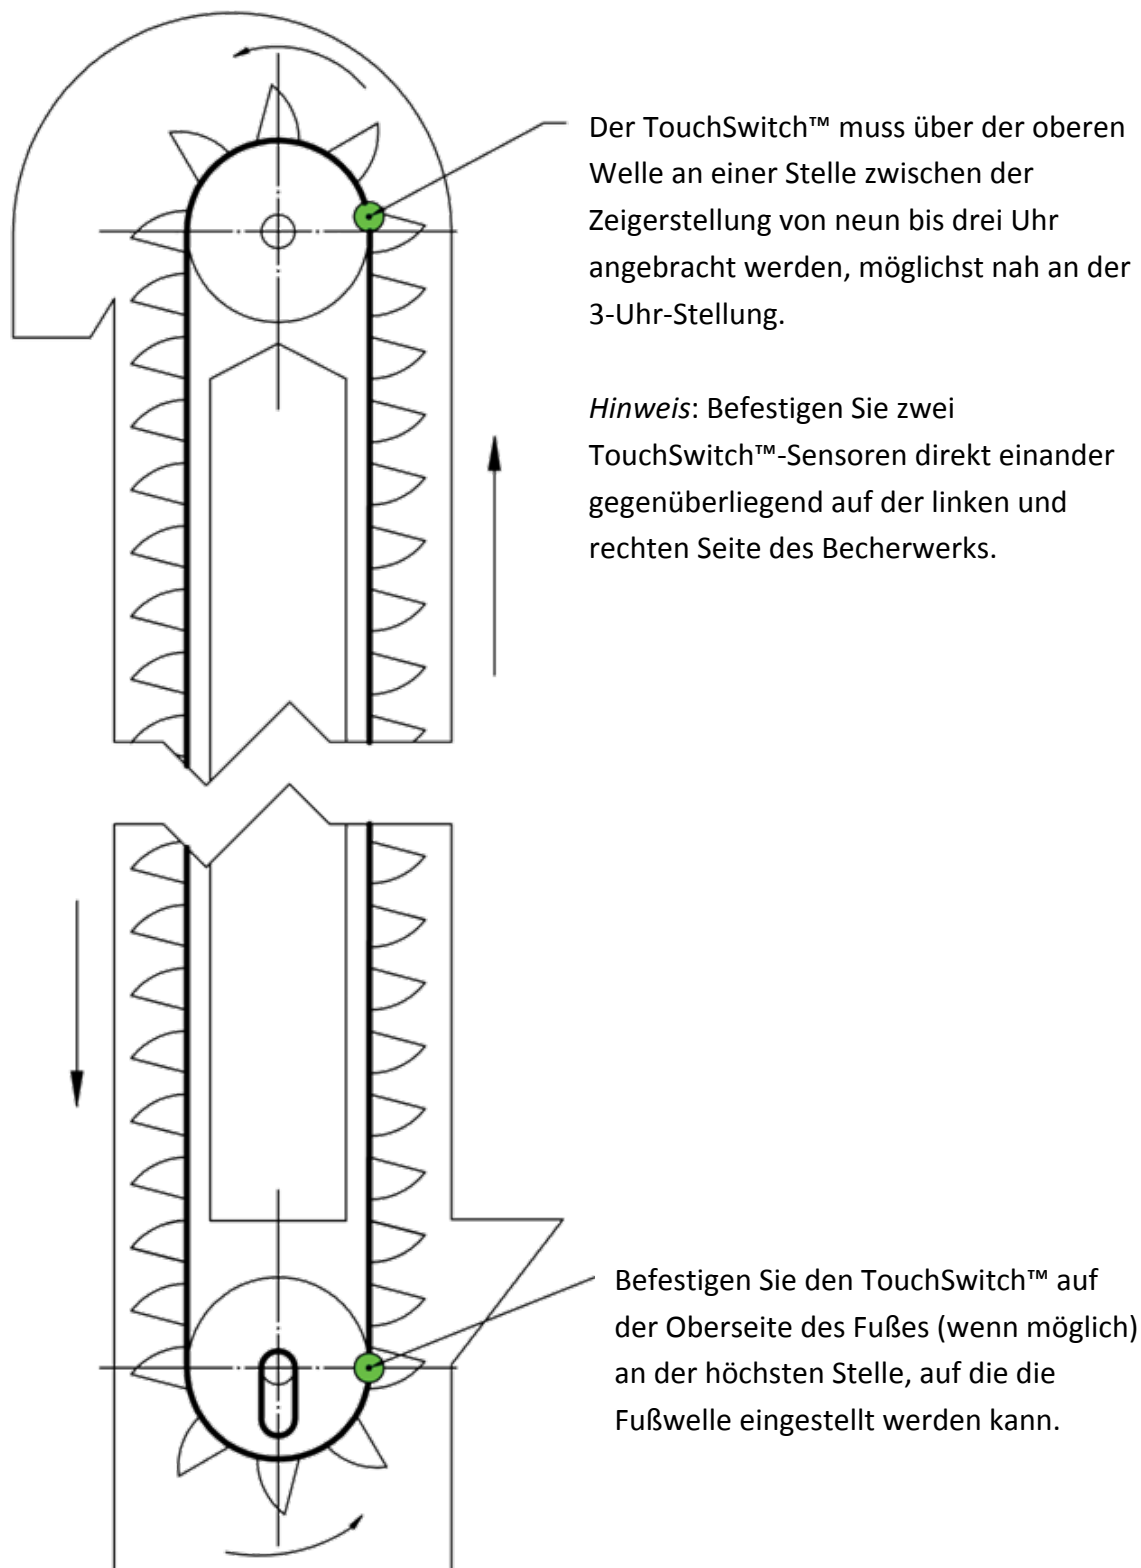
TouchSwitch-Befestigungspositionen – Becherwerksfuß
